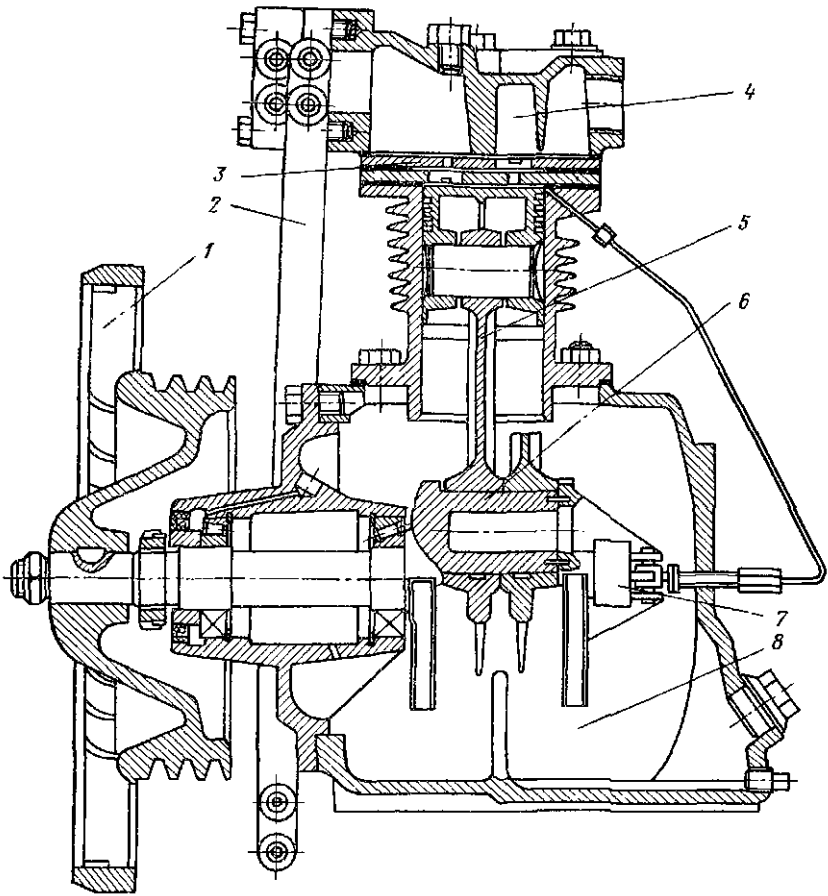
Продольный разрез У-образного компрессора с консольным коленчатым валом:
